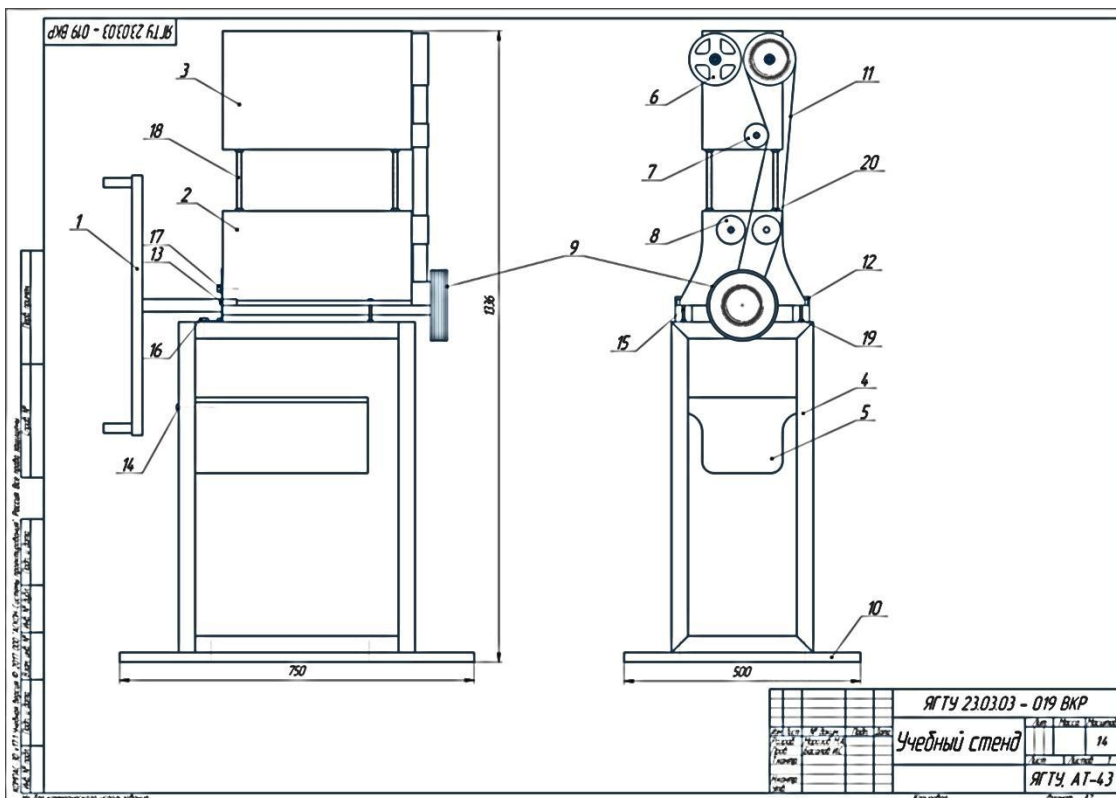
Чертеж станда двигателя внутреннего сгорания.
